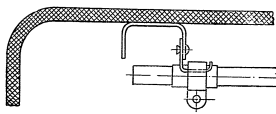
Установка верхнего датчика керсинометра в баке.
